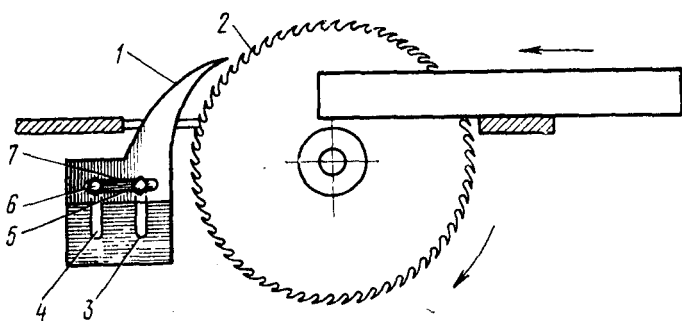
Установка расклинивающего ножа на круглопильных станках:
